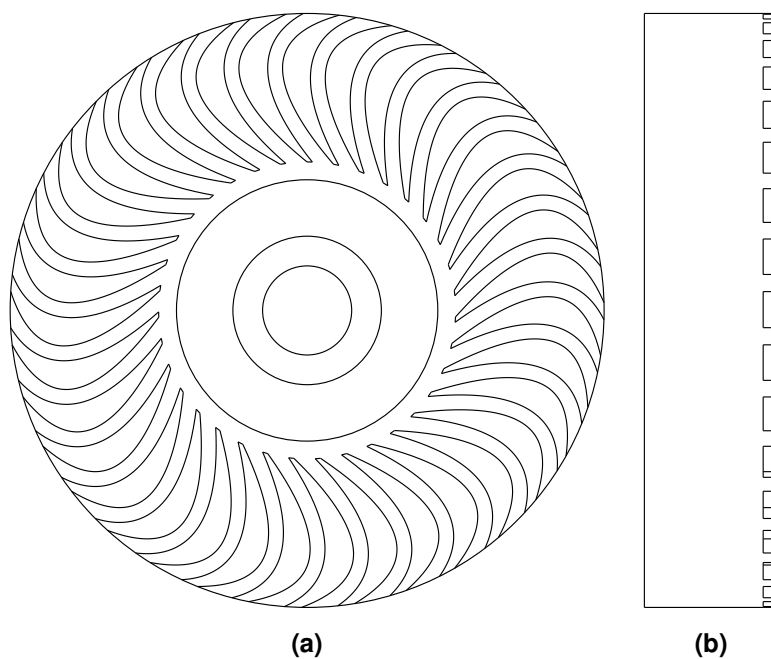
Zeichnung des 3D-gedruckten Rotorelements *3D_A* mit $\varnothing 20$ mm, 35 Schaufeln und einer Schaufelhöhe von 0,5 mm. (a): Draufsicht; (b): Seitenansicht.
